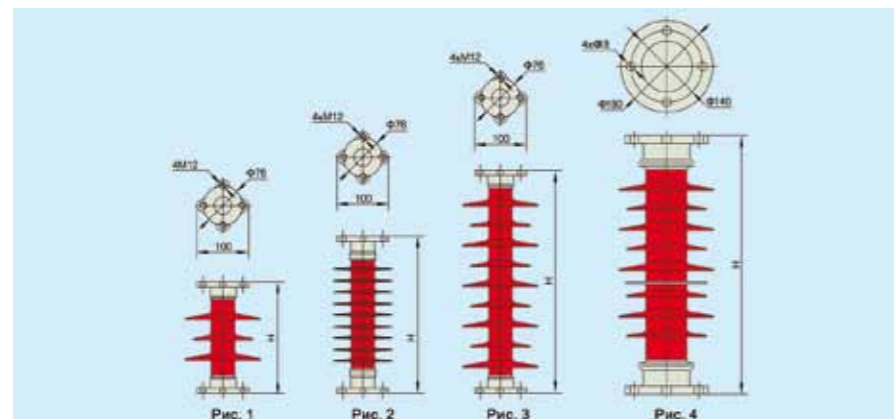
Внешний вид и размеры опорных штыревых изоляторов
